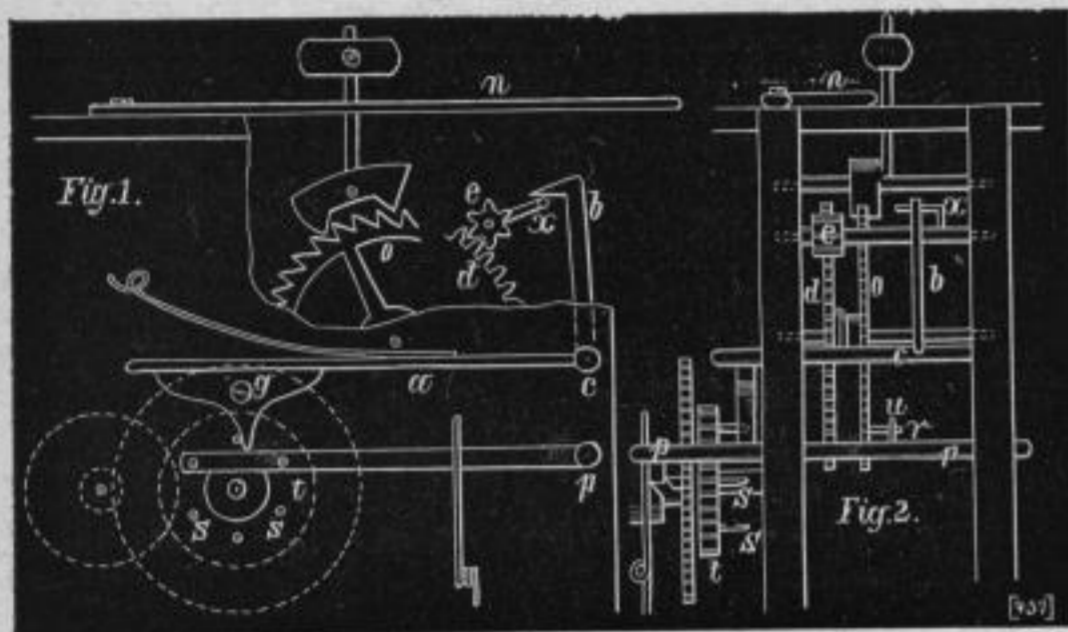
u. 2. Haupt- u. Seitenansicht des Weckerwerkes.
